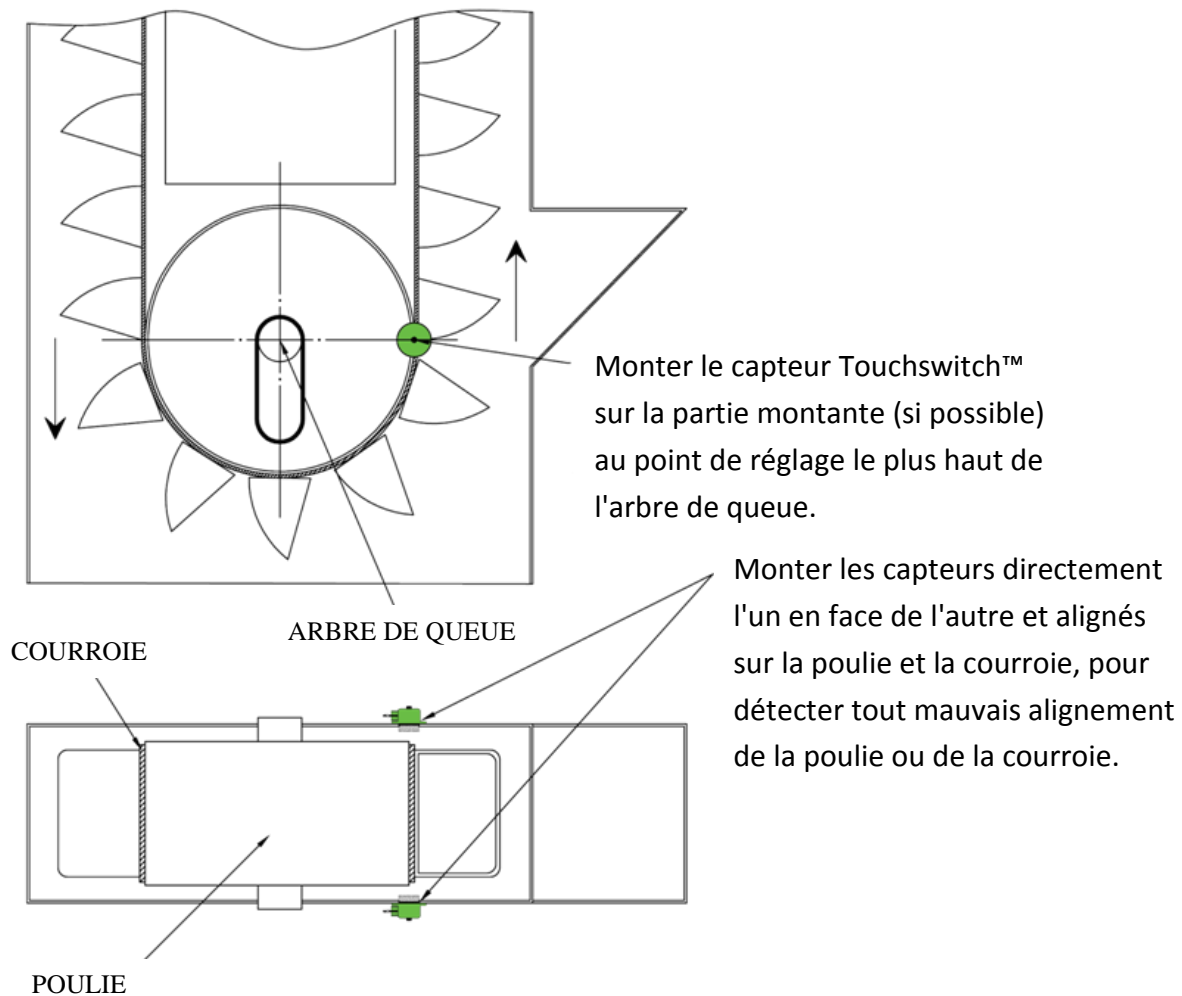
Position de montage des capteurs Touchswitch – Poulie de queue
